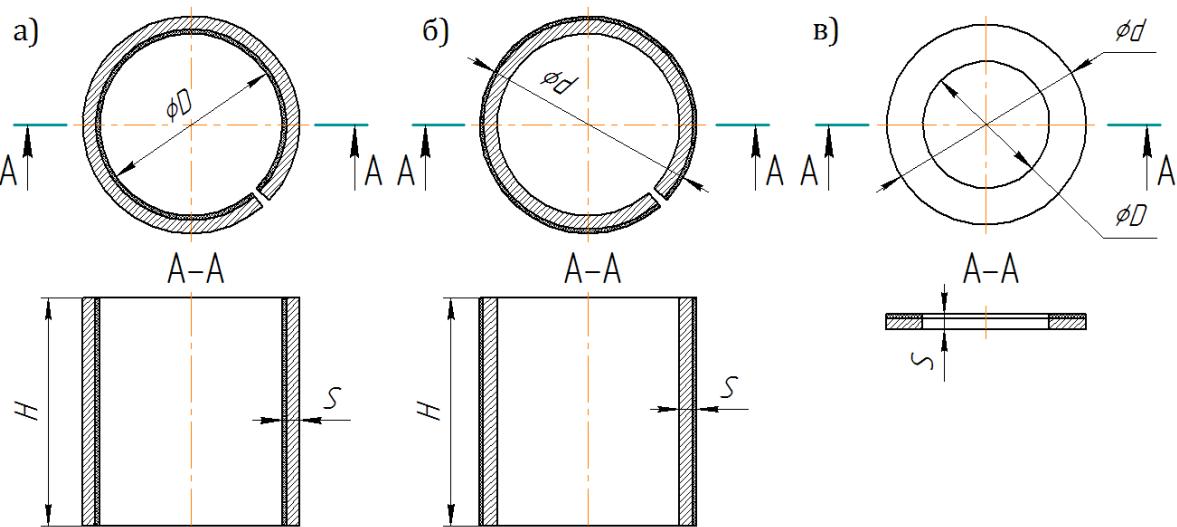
Общий вид: а – радиальный подшипник (направляющая) АР-У-8-В,
